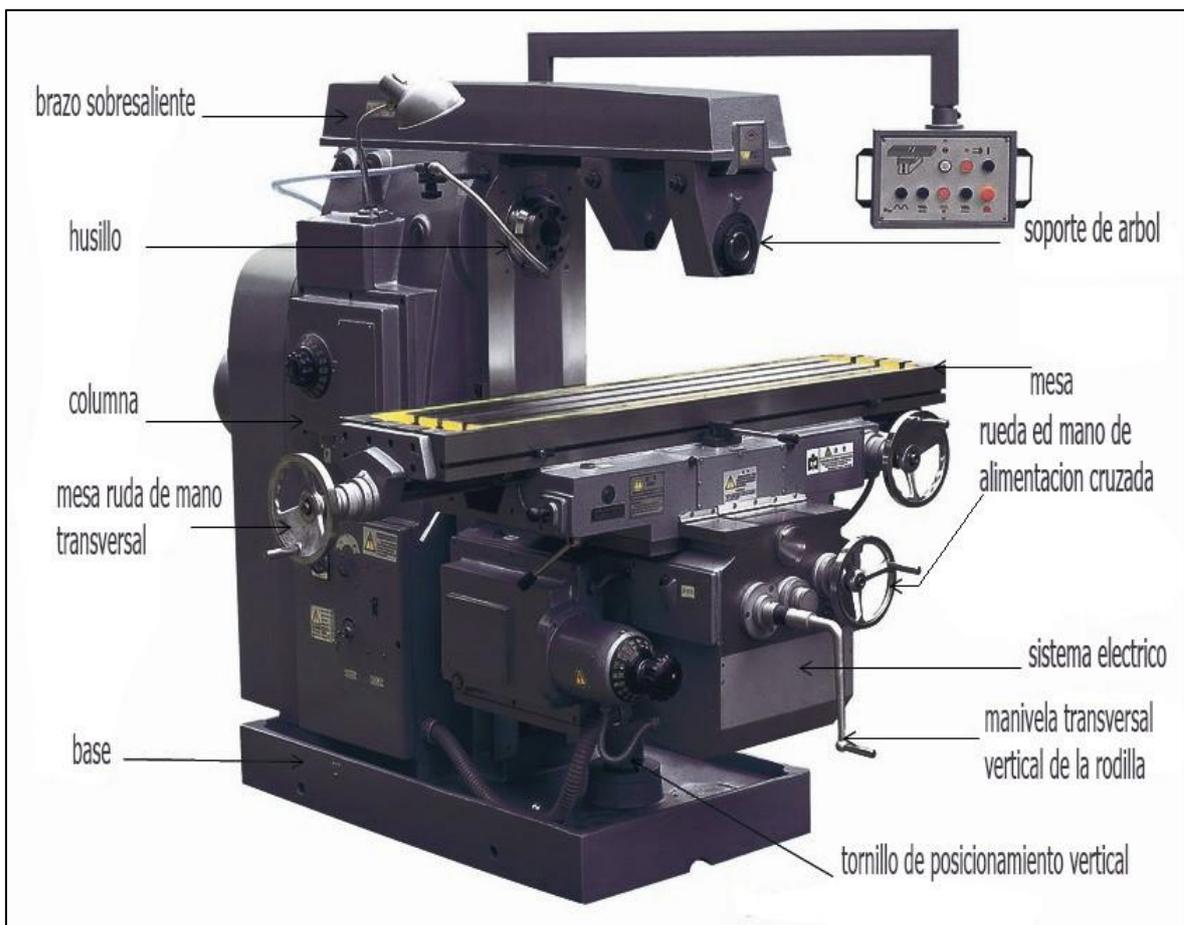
Fresadora Horizontal. Fuente: <https://www.machinecnc.online/fresadora-horizontal/>
